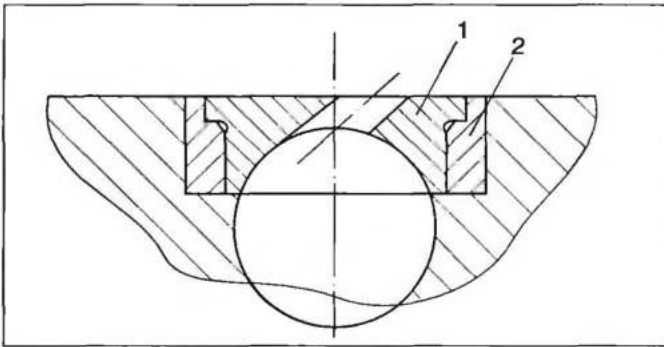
Ремонт гнезда вставки (крышки) форкамеры с помощью переходного кольца:
